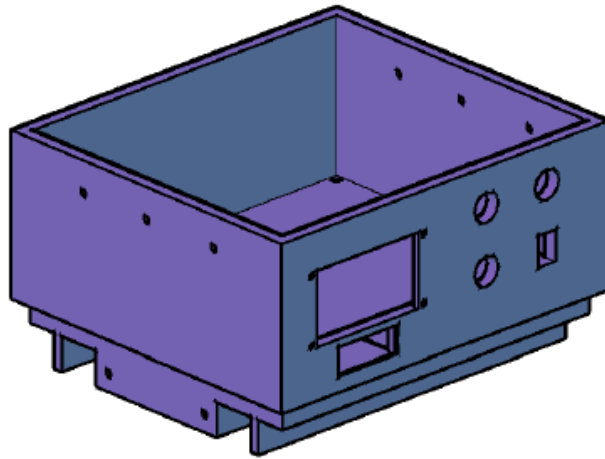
Diseño de la parte superior del prototipo en AutoCAD 3D.
